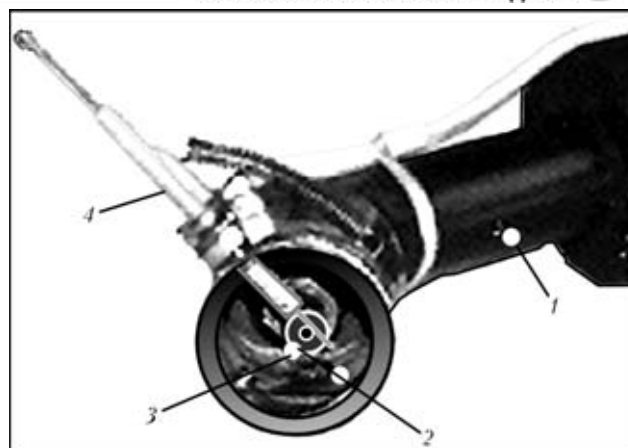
Внешний вид мундштука сварочной горелки с установленным на нем щупом: 1 — сварочная горелка; 2 — сопло сварочной горелки; 3 — щуп; 4 — мундштук
